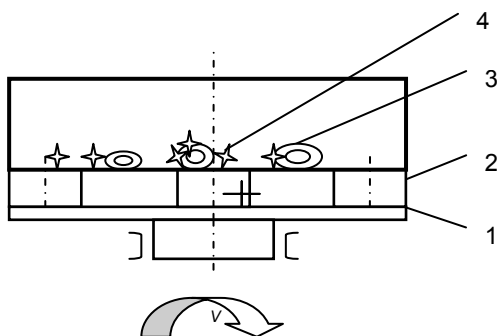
Схема установки для магнитно-абразивной обработки: 1 – вращающийся диск; 2 – постоянные магниты; 3 – обрабатываемые детали; 4 – наполнитель
